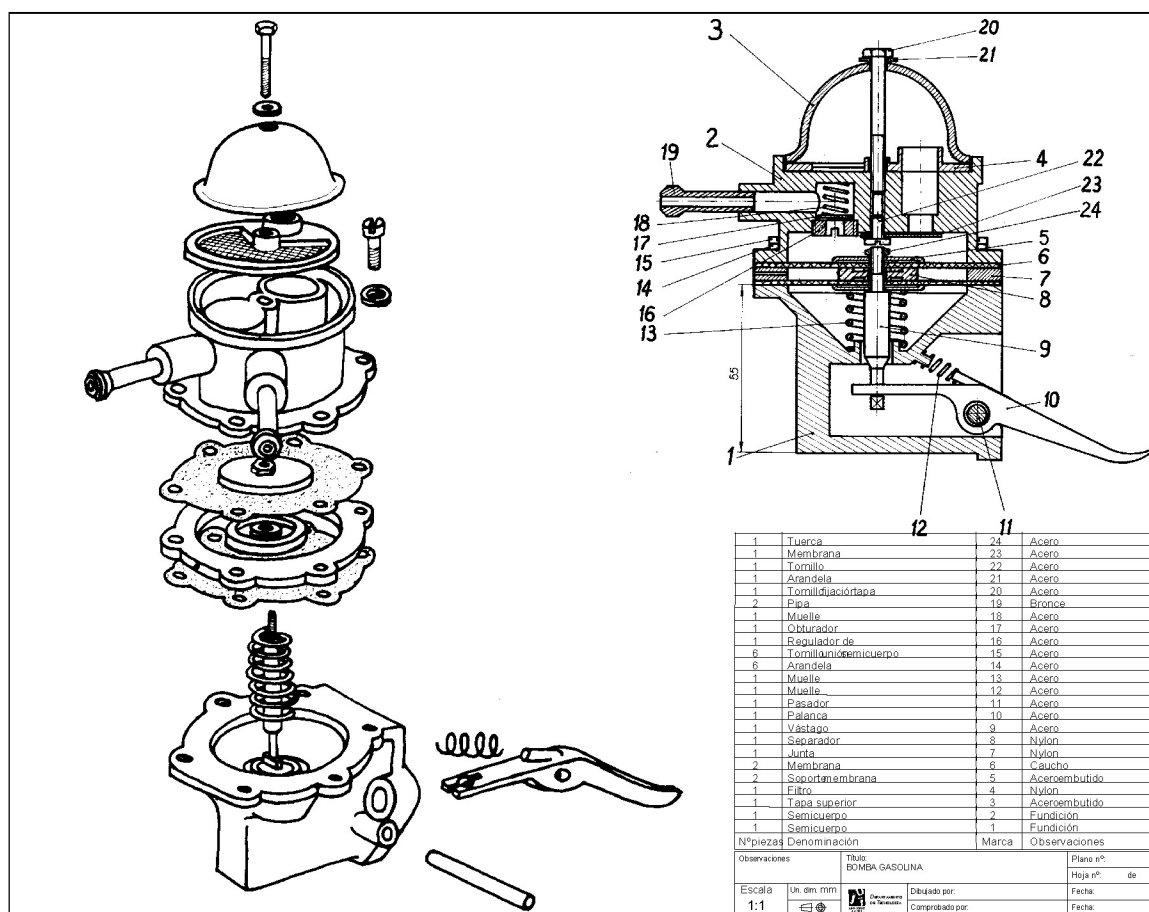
Dibujo de conjunto de una bomba de gasolina en explosión (izquierda) y montada (derecha)
